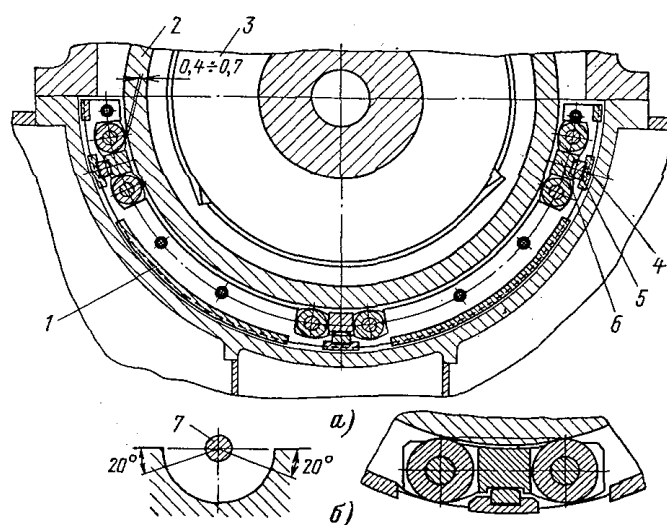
Установка зубчатого колеса валоповоротного пристрою на опорах качіння
